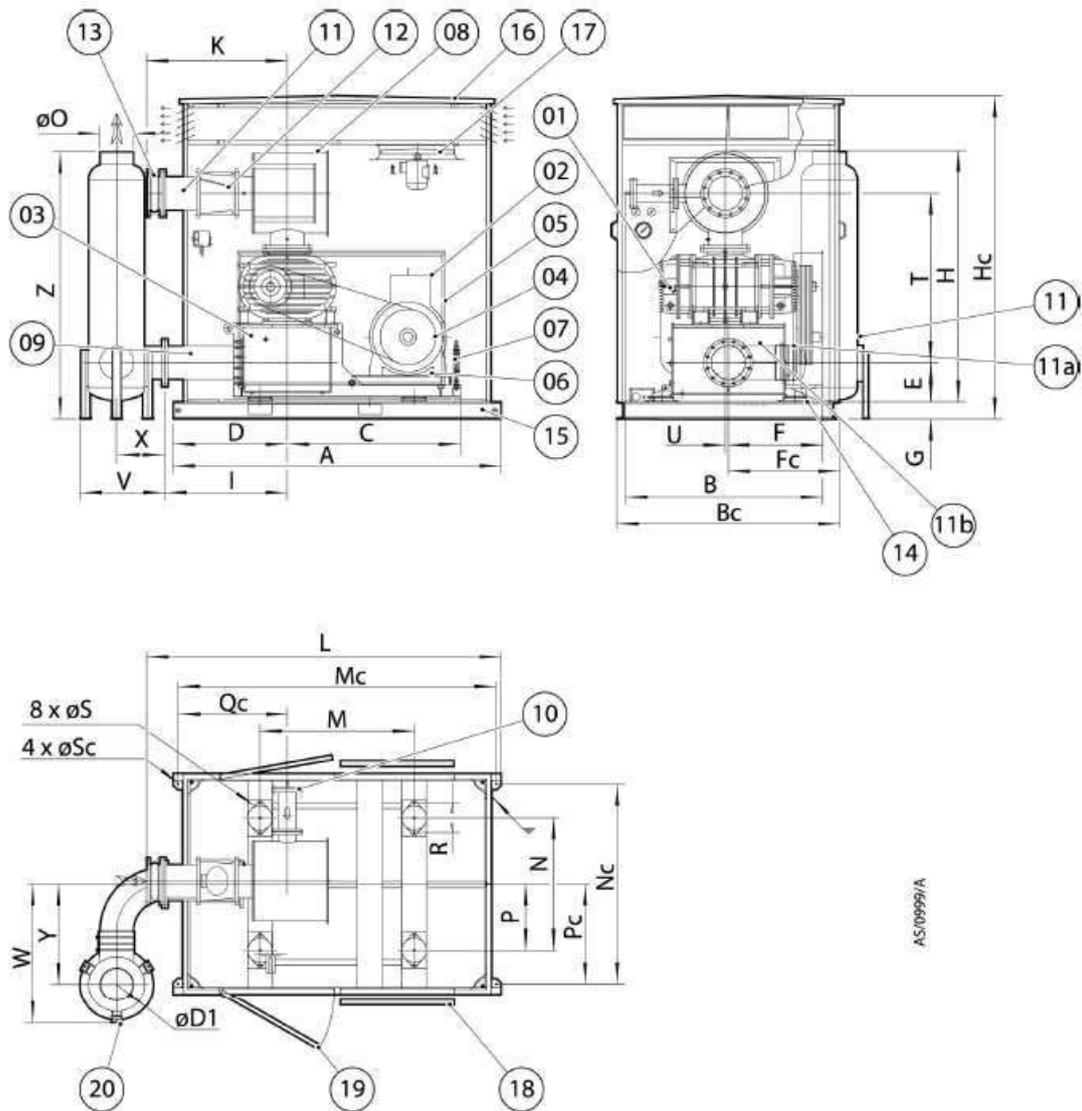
Габаритные размеры агрегатов нагнетания
